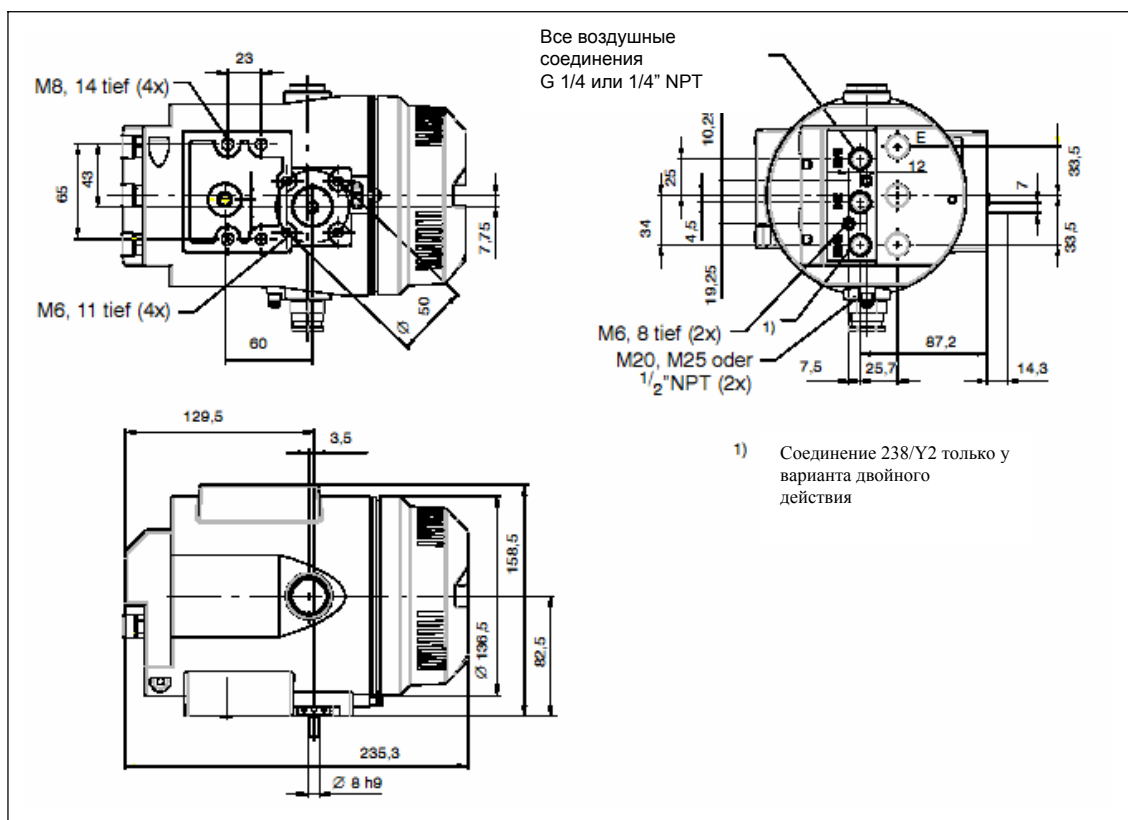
Габаритный чертеж позиционера в металлическом корпусе со взрывонепроницаемой конструкцией 6DR5xx5
